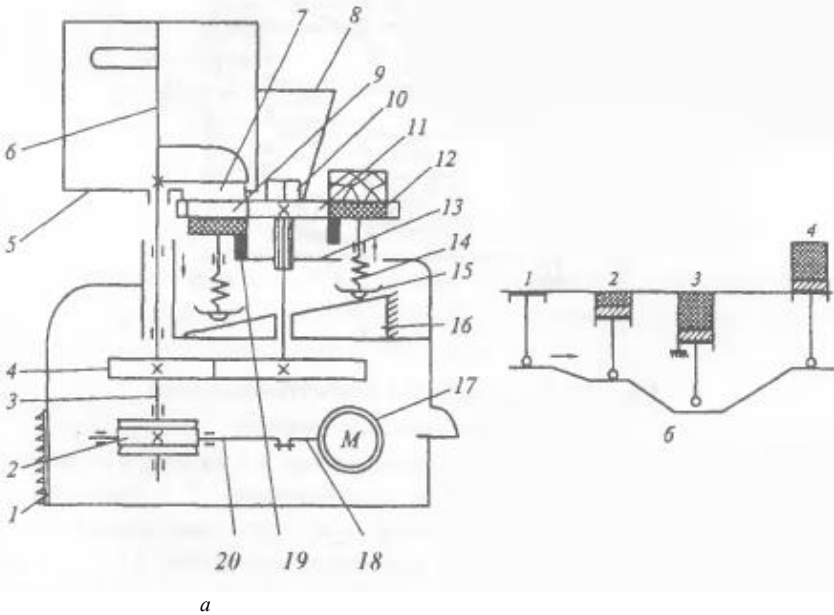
Котлетоформувальна машина: а – принципова схема; б – циклограма руху поршня формуючого стола; 1 – корпус; 2 – черв'ячний редуктор; 3 – вал шнека-живильника; 4 – циліндрична передача; 5 – бункер для фаршу; 6 – шнек-живильник; 7 – отвір у бункері; 8 – бункер для сухарів; 9 – отвір; 10 – регулювальний гвинт; 11 – формуючий стіл; 12 – поршень; 13 – планка; 14 – пружини; 15 – штовхальник; 16 – торцевий копер; 17 – електродвигун; 18 – вал електродвигуна; 19 – упор; 20 – вал черв'ячного редуктора
